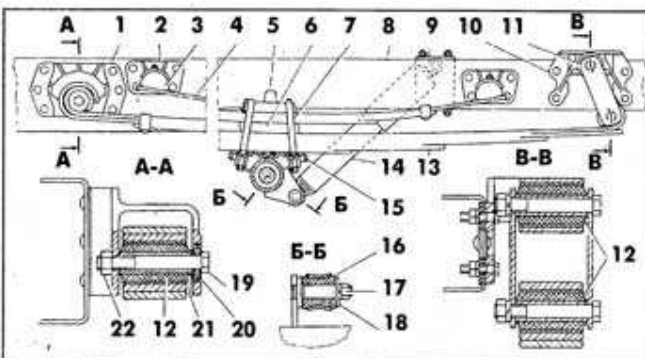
Задняя подвеска автомобилей (кроме автобусов) типа 4x2: 1, 2, 9 и 10 – кронштейны; 3 – подушка; 4 – дополнительная рессора; 5 – наклад-ка; 6 – прокладка; 7 – стремянка; 8 – лонжерон рамы; 11 – серьга; 12 – резинометаллические шарниры; 13 – рессора; 14 – амортизатор; 15 – подушка рессоры; 16 – резиновая втулка; 17 и 22 – гайки; 18, 20 и 21 – шайбы; 19 – болт.
